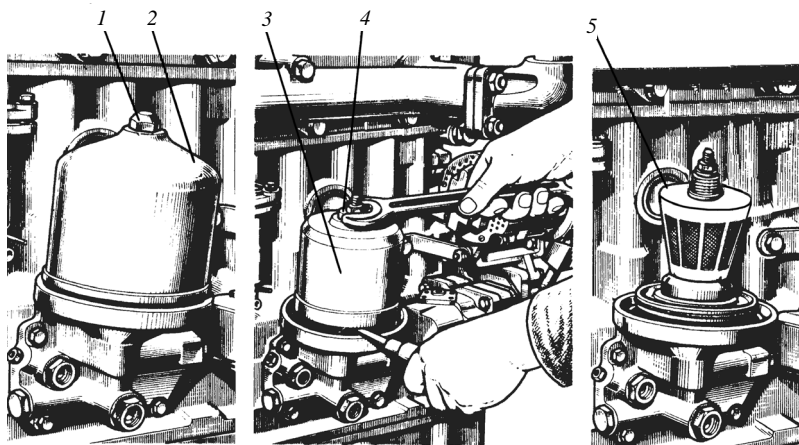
Очистка ротора центробежного масляного фильтра двигателя:
